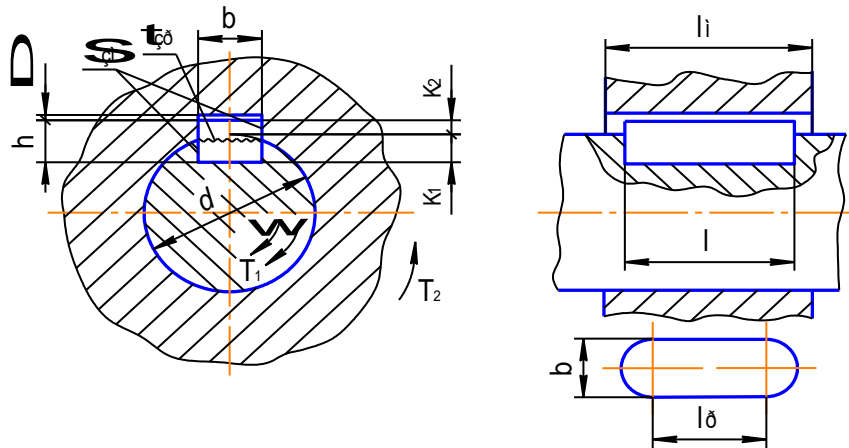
Конструкція шпонкового з'єднання з призматичною шпонкою
